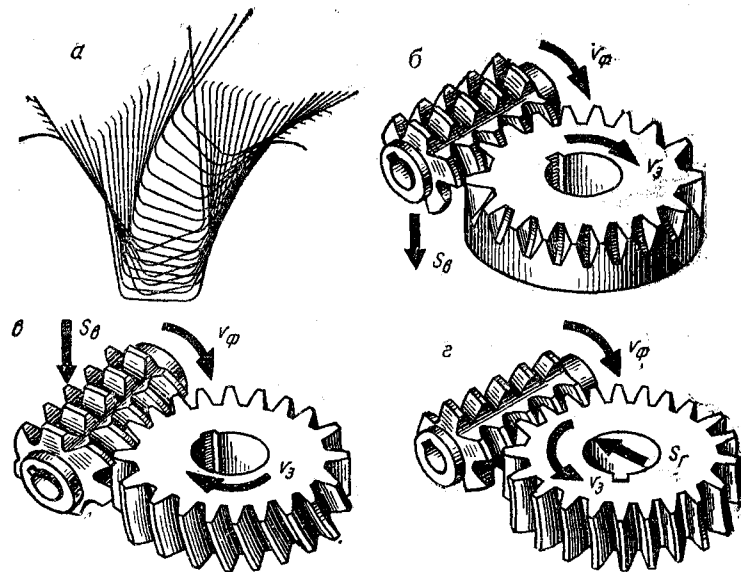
Схемы нарезания зубчатых колес червячной модульной фрезой
